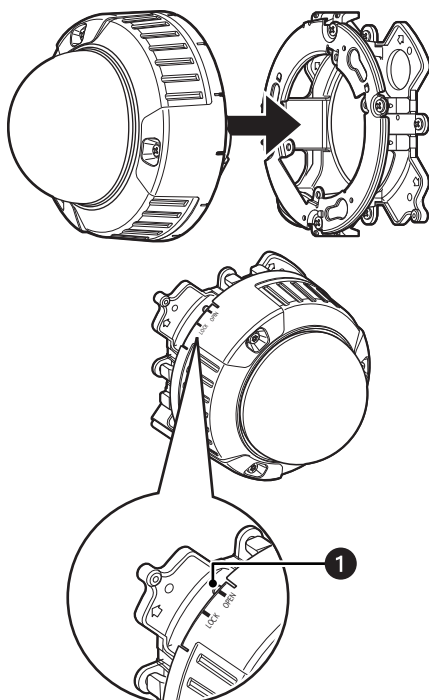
Установка камеры на крепление камеры (поверхностный монтаж)
